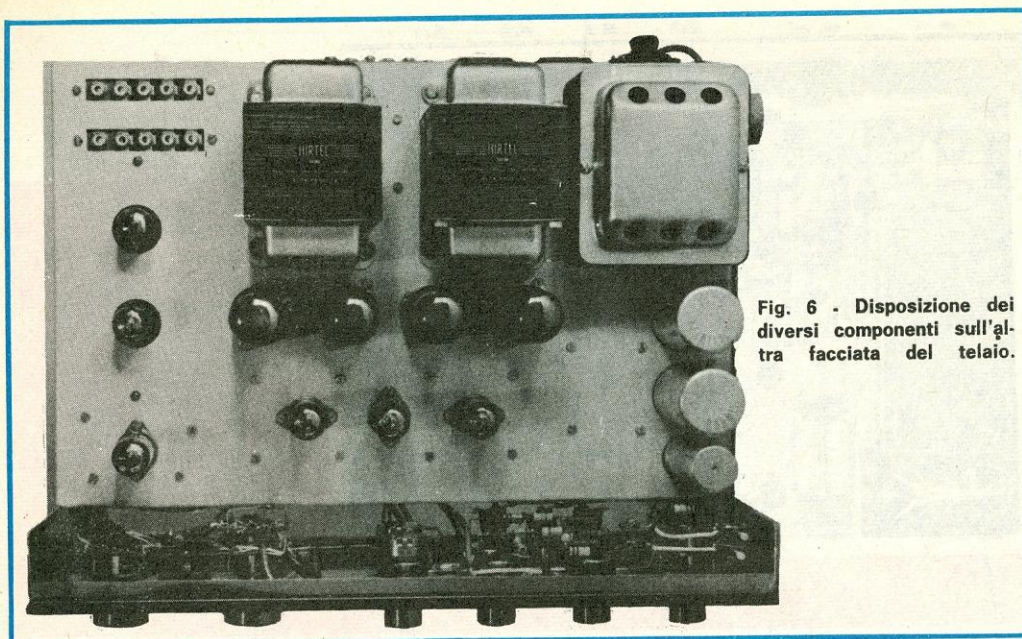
Disposizione dei diversi componenti sull'altra facciata del telaio.
